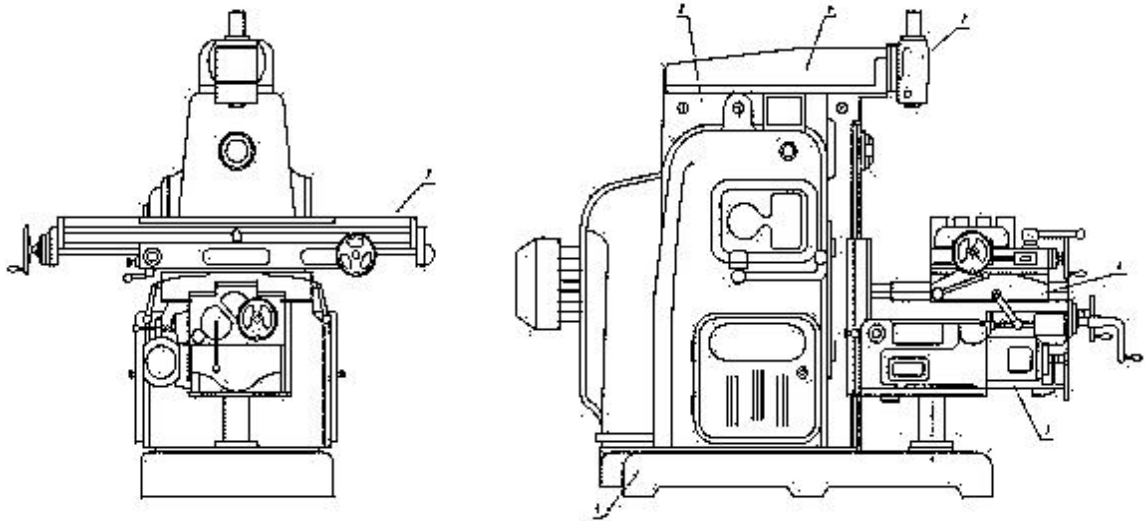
Загальний вид модернізованого верстата мод. 6M821 – основа, 2 – станина, 3 – консоль, 4 – полозок, 5 – стіл, 6 – хобот, 7 – фрезерна головка.
